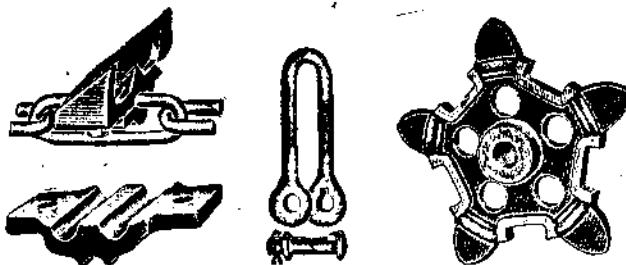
Башмак с зубьями, соединительная часть для цепи и звездочка.
